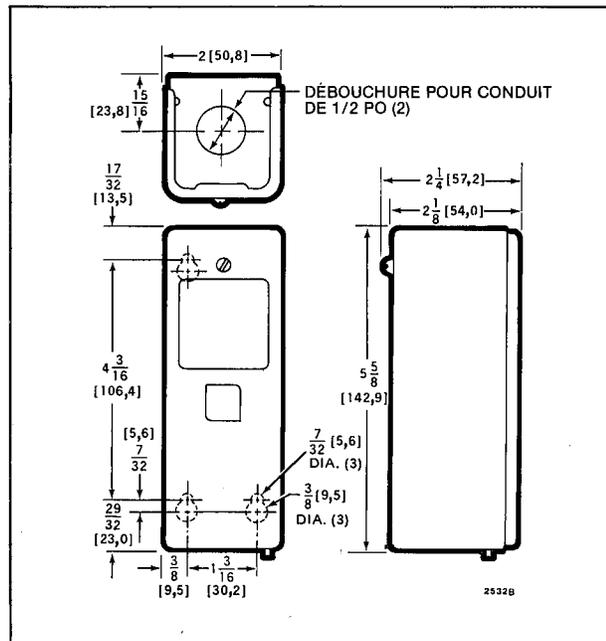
DIMENSIONS DES T4031 ET T6031 EN POUÇES [mm].
